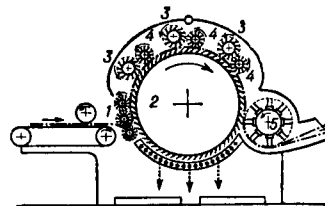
Щипально-смешивающая машина: 1 — питающие цилиндры; 2 — барабан; 3 — рабочие валики; 4 — очистительный валик; 5 — ветрянка.
